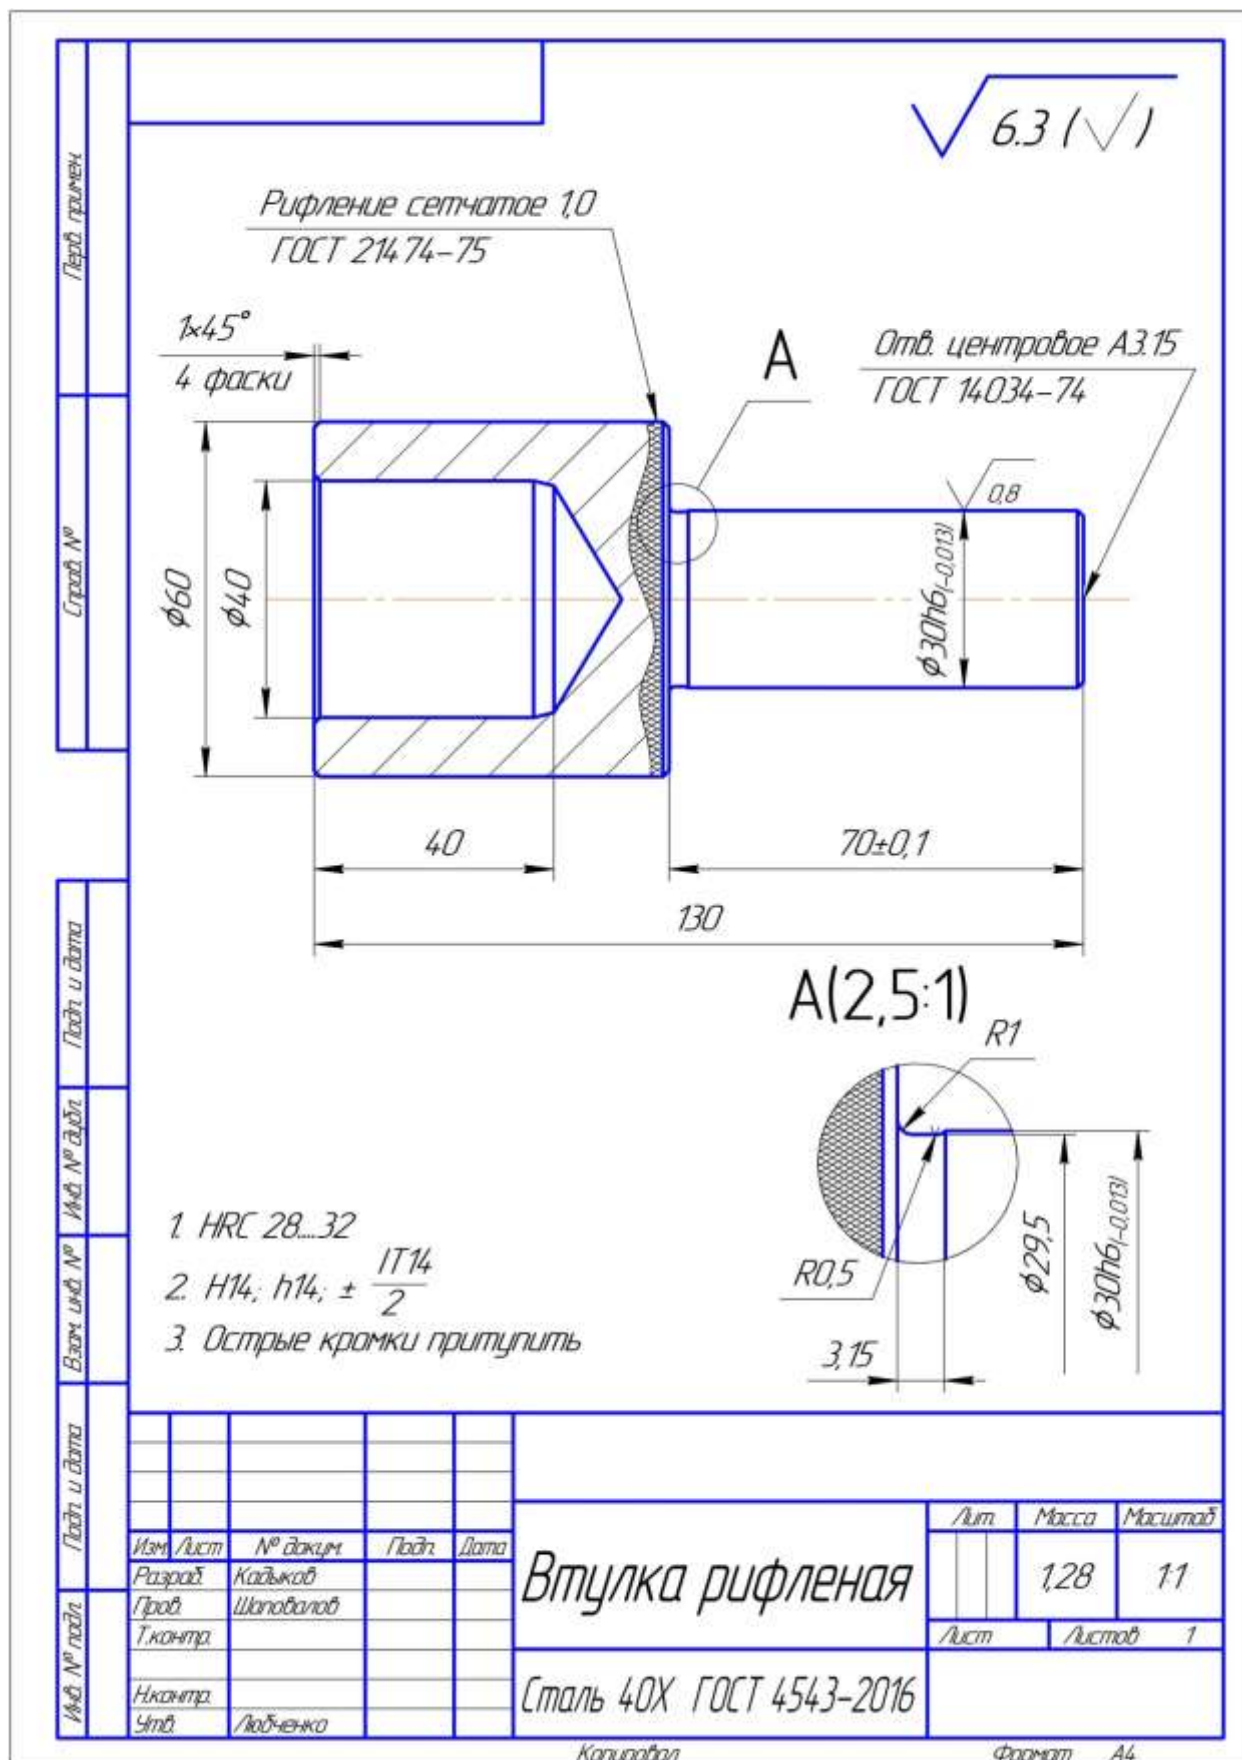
Кресленик деталі «Втулка рифлена»
